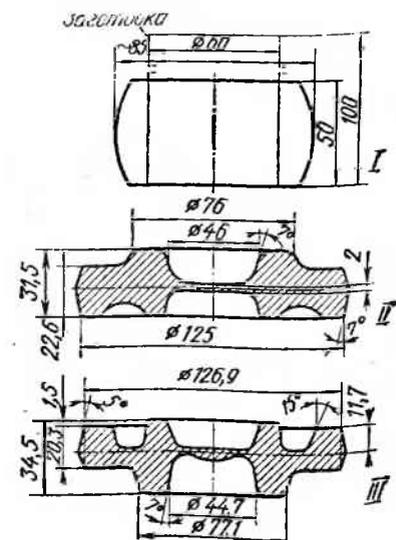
Переходы штамповки зубчатого колеса на КГШП:
